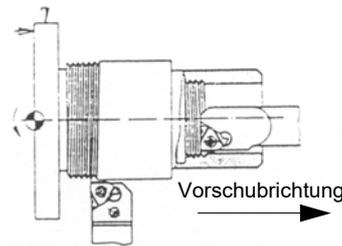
Linksgewinde bei Rechtslauf der Maschinenspindel
